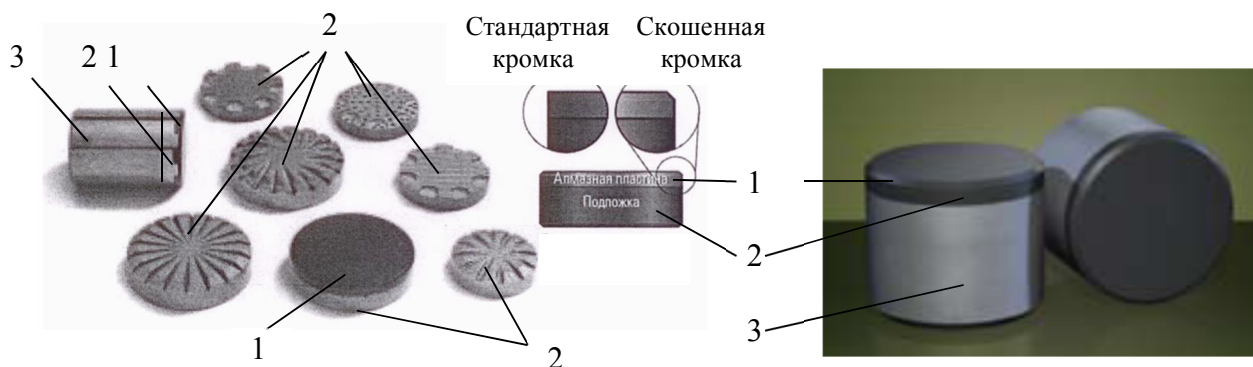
Виды пластинок и резцов *PDC* и возможные формы: 1 – поликристаллические алмазы; 2 – подложка из твердого сплава; 3 – корпус резца
